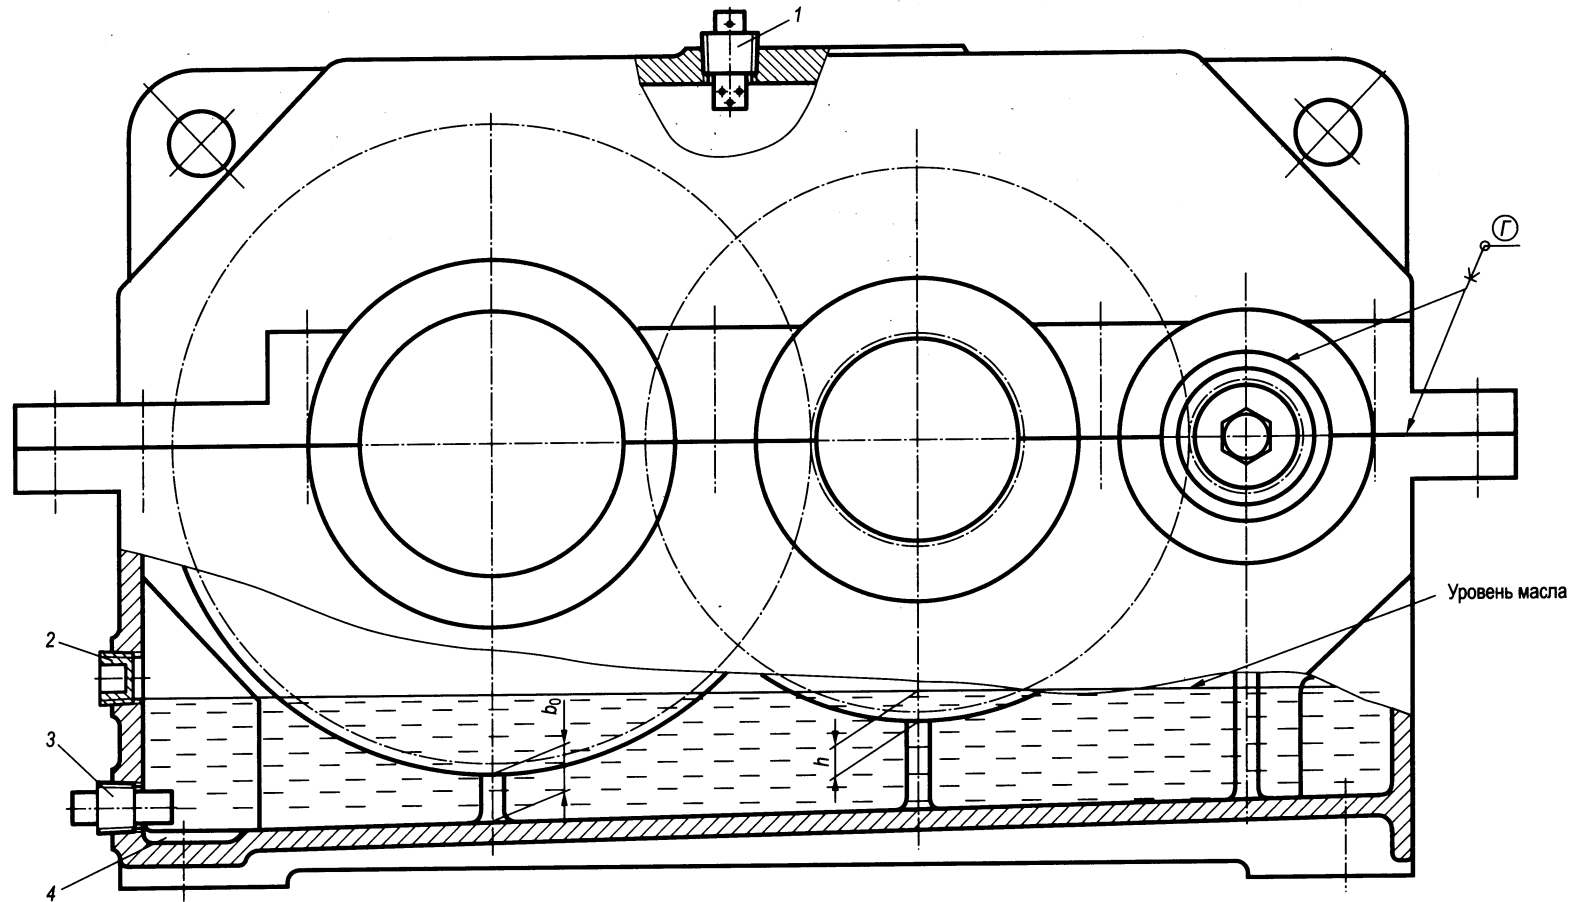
Двухступенчатый редуктор по развернутой схеме с погружением быстроходного колеса в масляную ванну:
